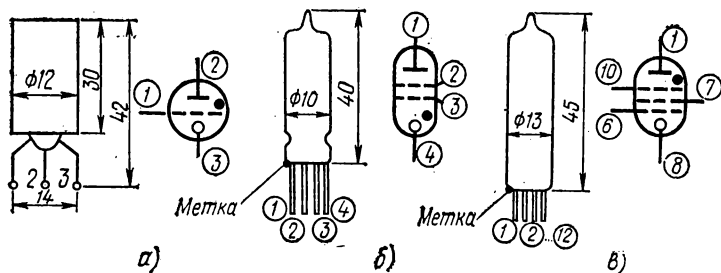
Габаритные чертежи и цоколевка тиратронов тлеющего разряда:
